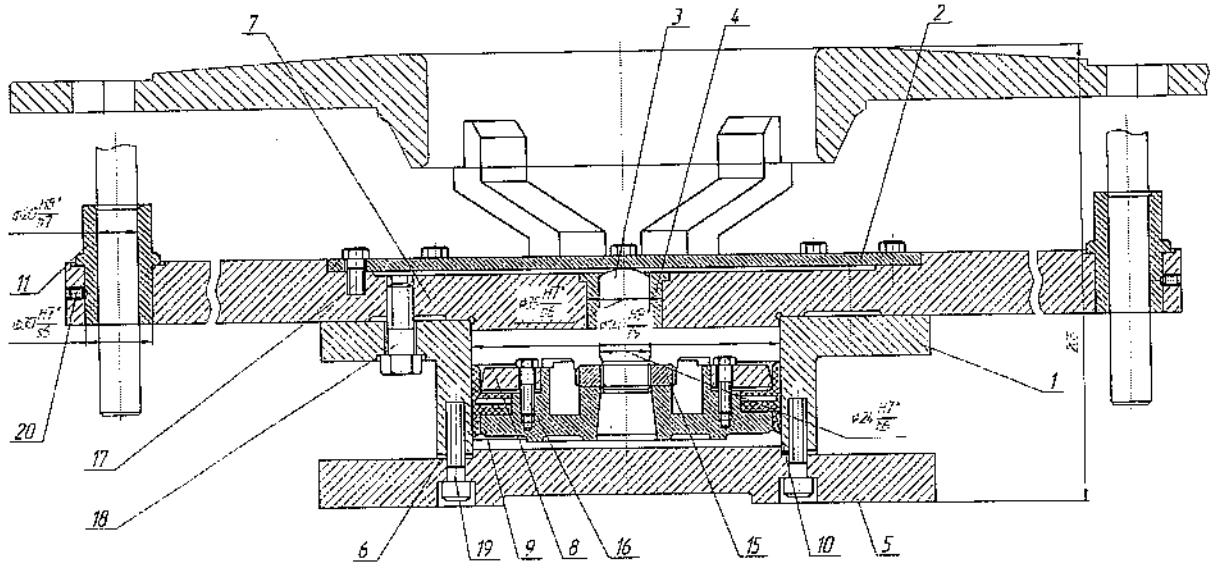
Приспособление для сверления 8-ми отверстий
